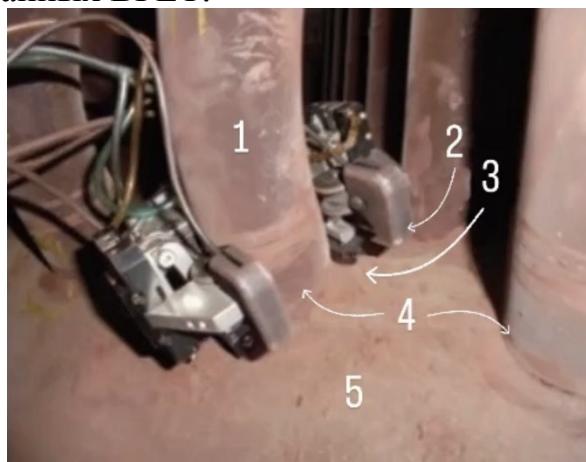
Осмотр шва приварки трубы к коллектору: 1 – труба, 2 – камера, 3 – датчик, 4 – сварной шов, 5 – коллектор [1, 2]
